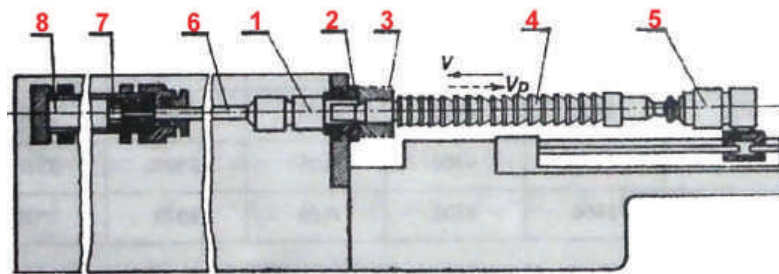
Skema e makinës për tërheqje horizontale: 1-shtrënguesi; 2-mbështetësi; 3-pjesa; 4-tërheqësi; 5-shtrënguesi; 6-leva; 7-pistoni; 8-cilindri
